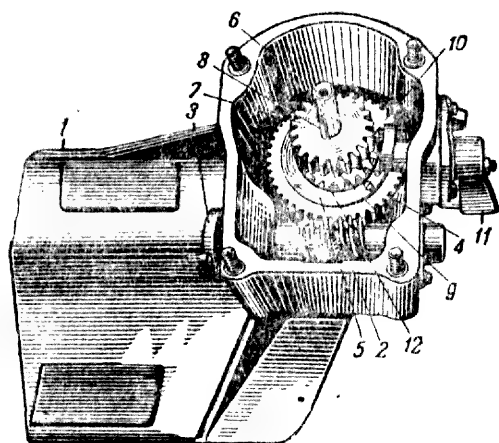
Механизм вертикального вращения (вид со стороны штангиста; крышка с зажимной гильзой снята):
